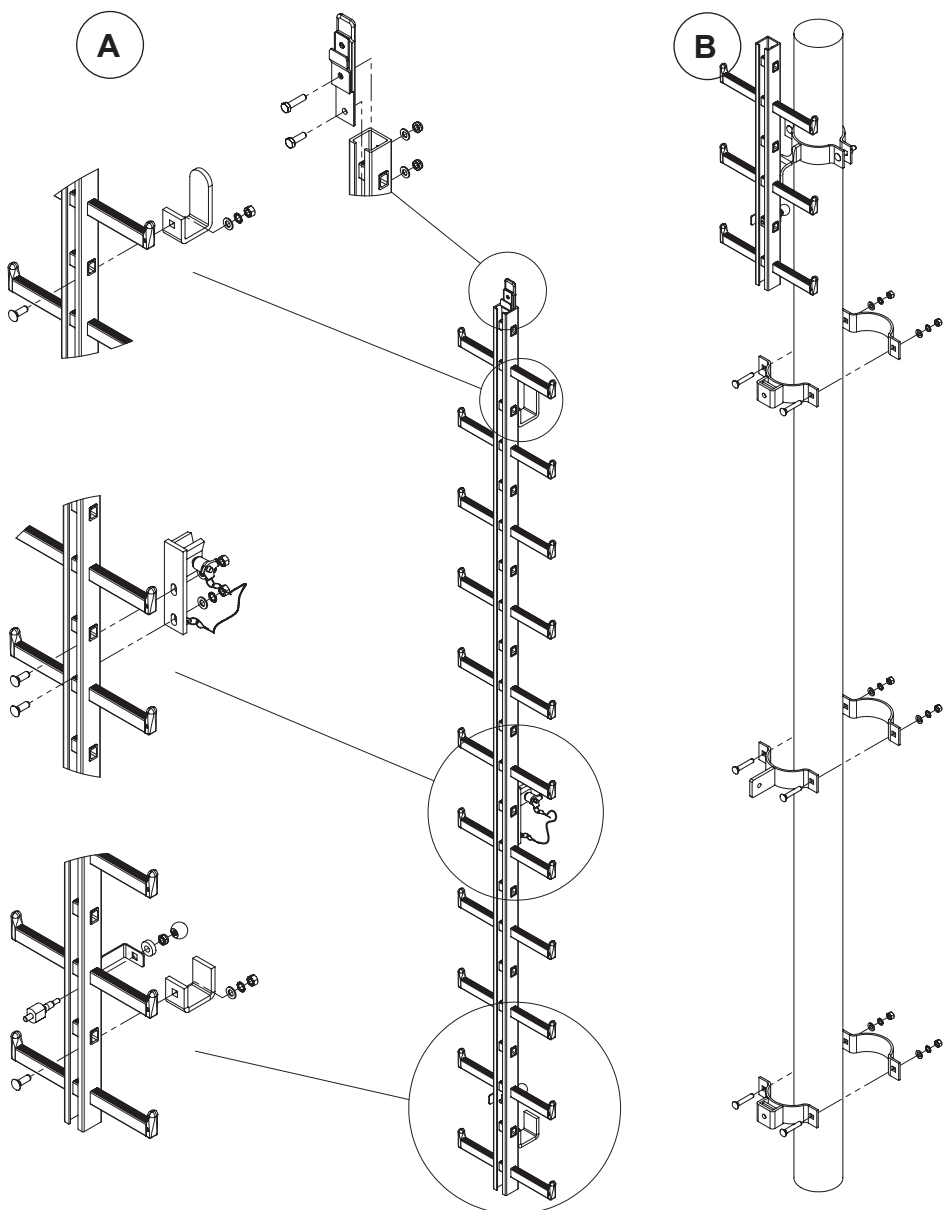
Montaggio scala di inserimento: A: Montaggio staffe
